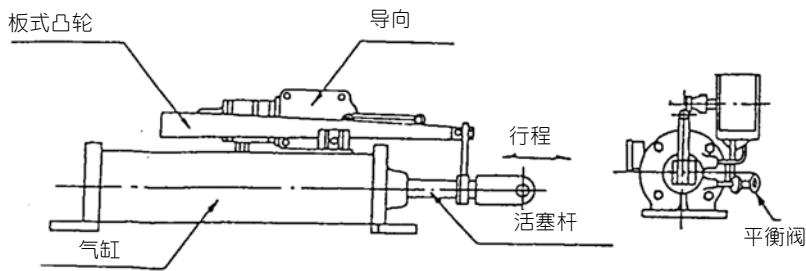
带板式凸轮反馈机构的水平 G-O-Motor
